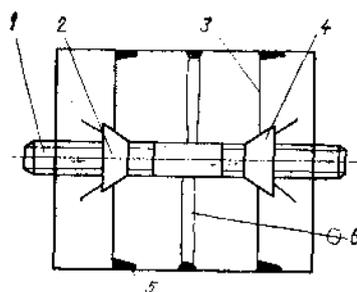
Схема забезпечення співвісності під час зварювання частин кожуха шнека: 1 — вісь; 2 — конусна гайка; 3 — центруючі диски; 4 — зварювані частини кожуха шнека; 5 — місця зварювання.
